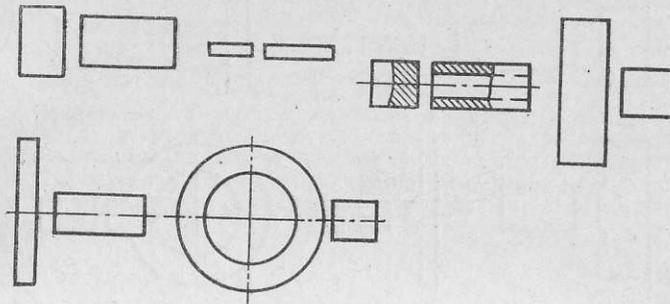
Типы сварных соединений стыковой сварки оплавлением
